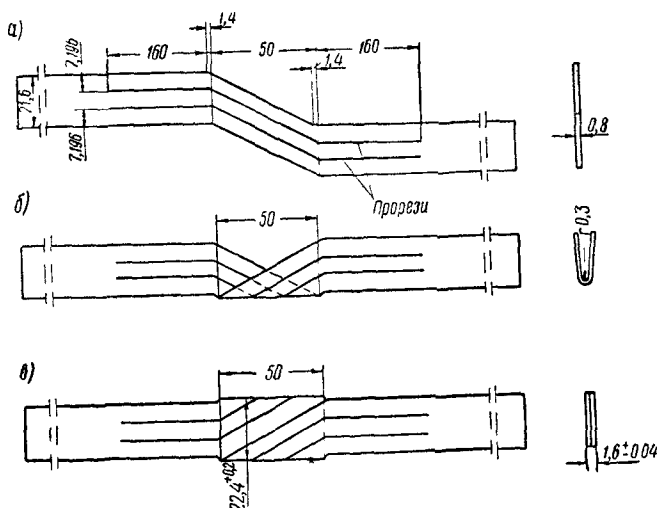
Заготовка ший якорных катушек двигателей НБ-411 и ДПЭ-400:
